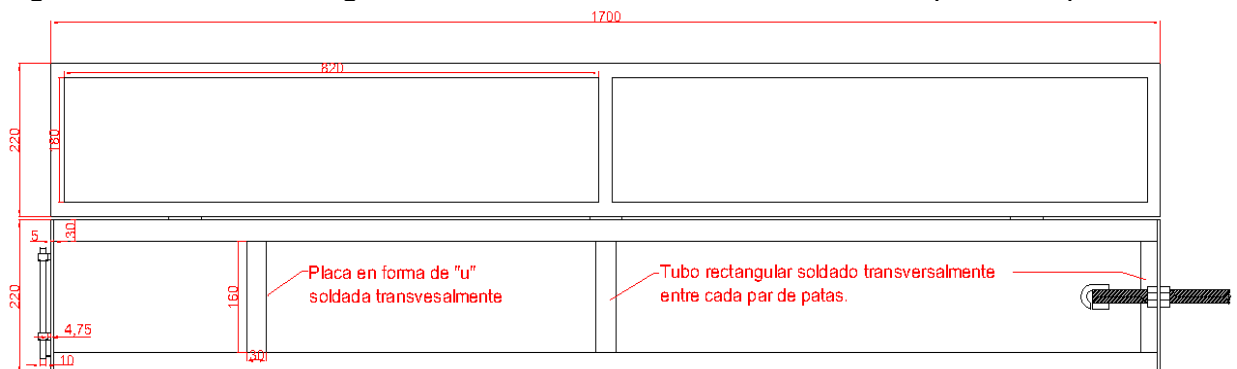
Vista frontal: Patas y marco soldados sobre los perfiles.
